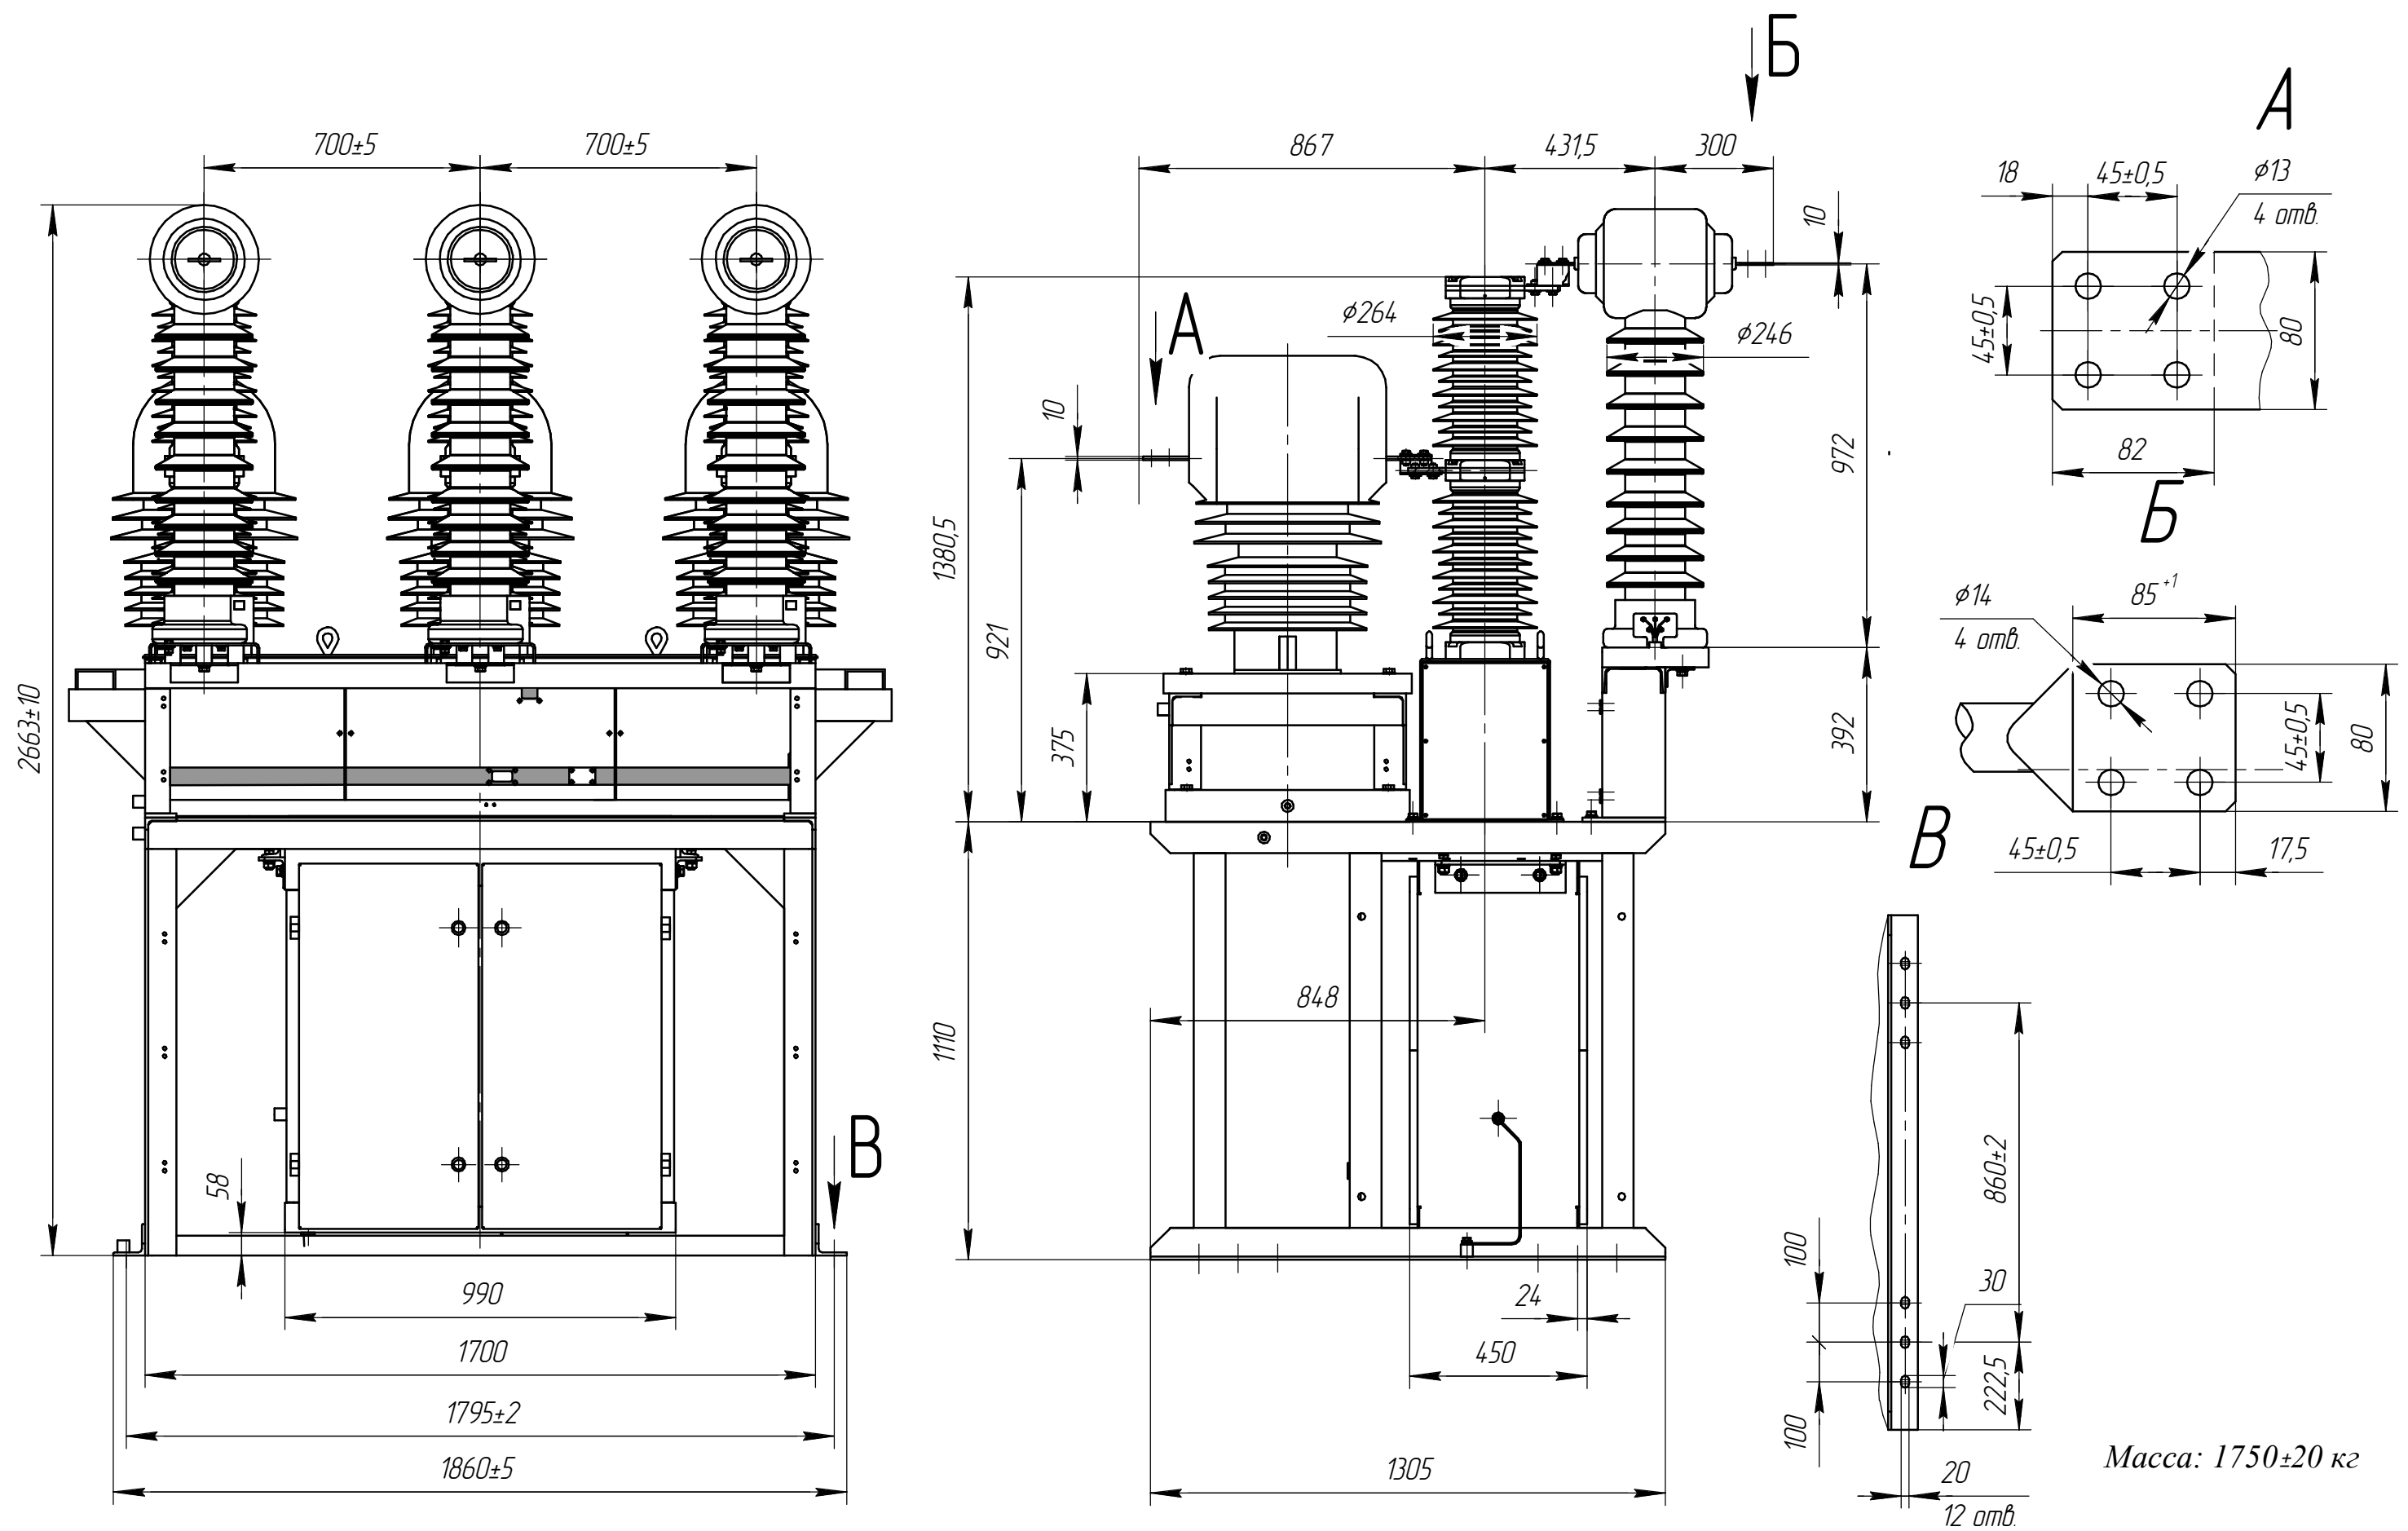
Габаритные, установочные и присоединительные размеры выключателя типоразмера ВР35НТ-35-25/1600-3/3 УХЛ1 с тремя встроенными трансформаторами тока ТОЛ-35 III-III УХЛ1 со стороны нижних контактов и ТОЛ-35 III-IV-2; 4; 6; 8 со стороны нижних контактов
